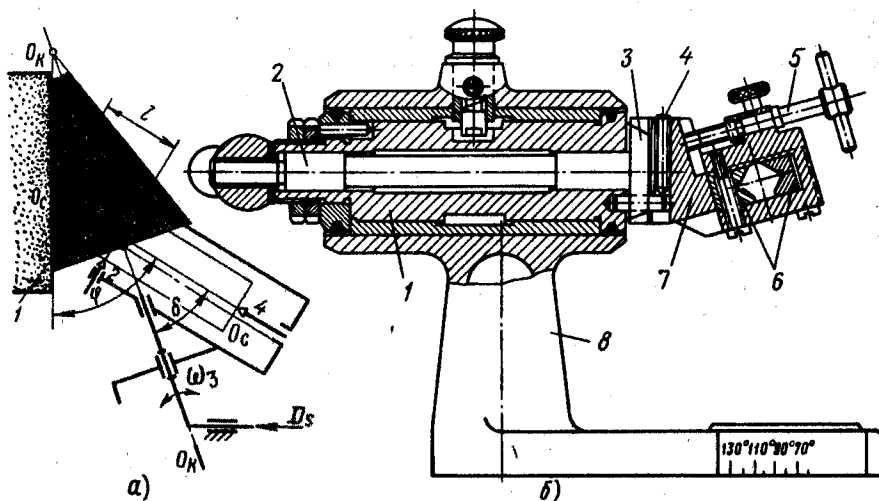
Приспособление для заточки сверла с конической задней поверхностью
